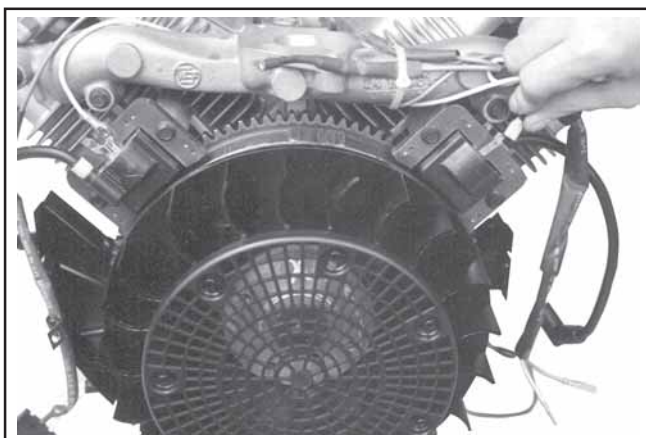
Collegamento dei cavi generali sulle bobine di accensione standard.
